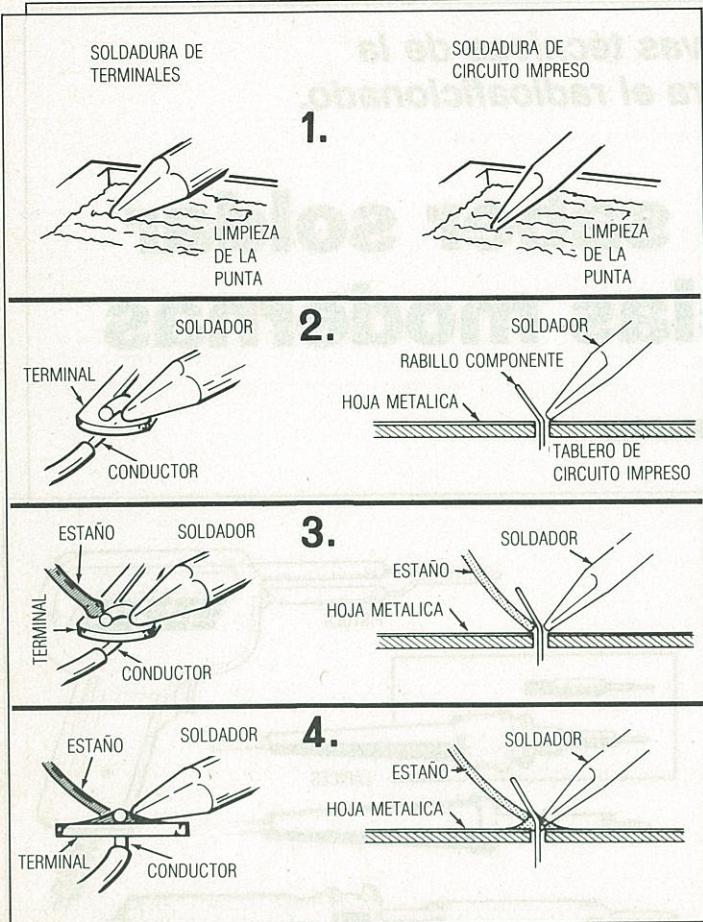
Cuatro etapas para obtener una buena soldadura.
